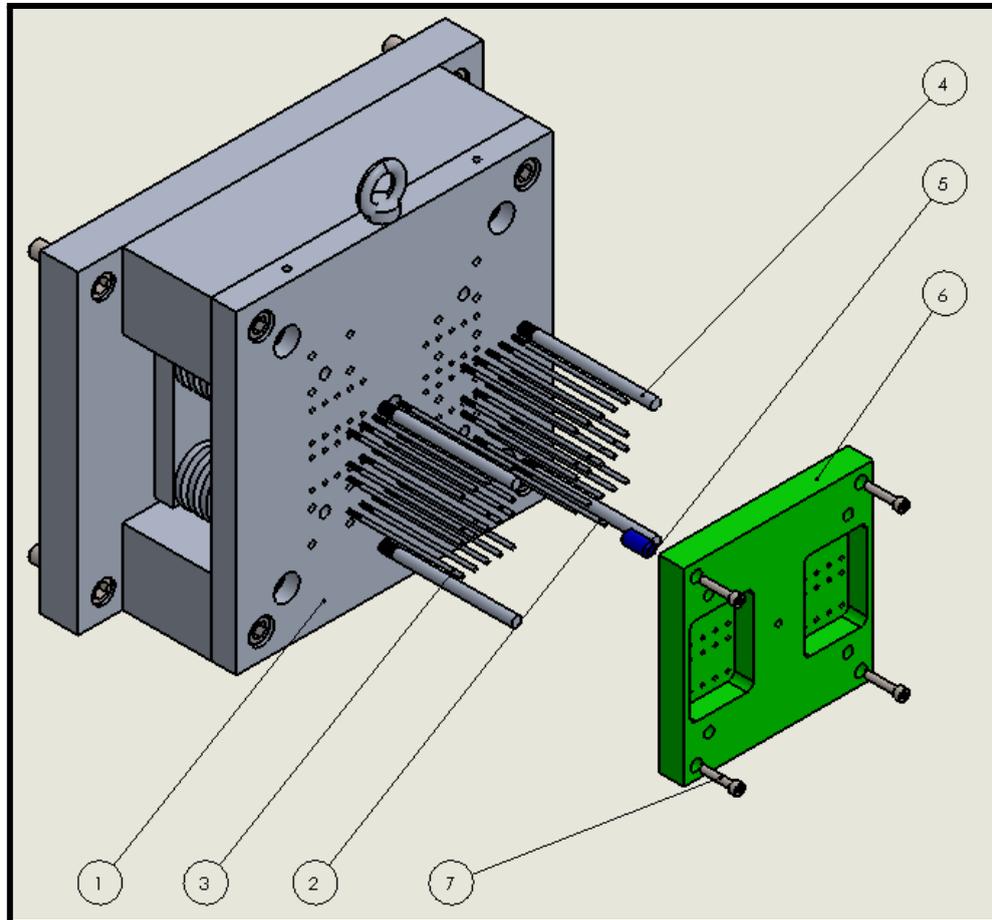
M. Vista explosionada de la configuración 3 del portamolde
